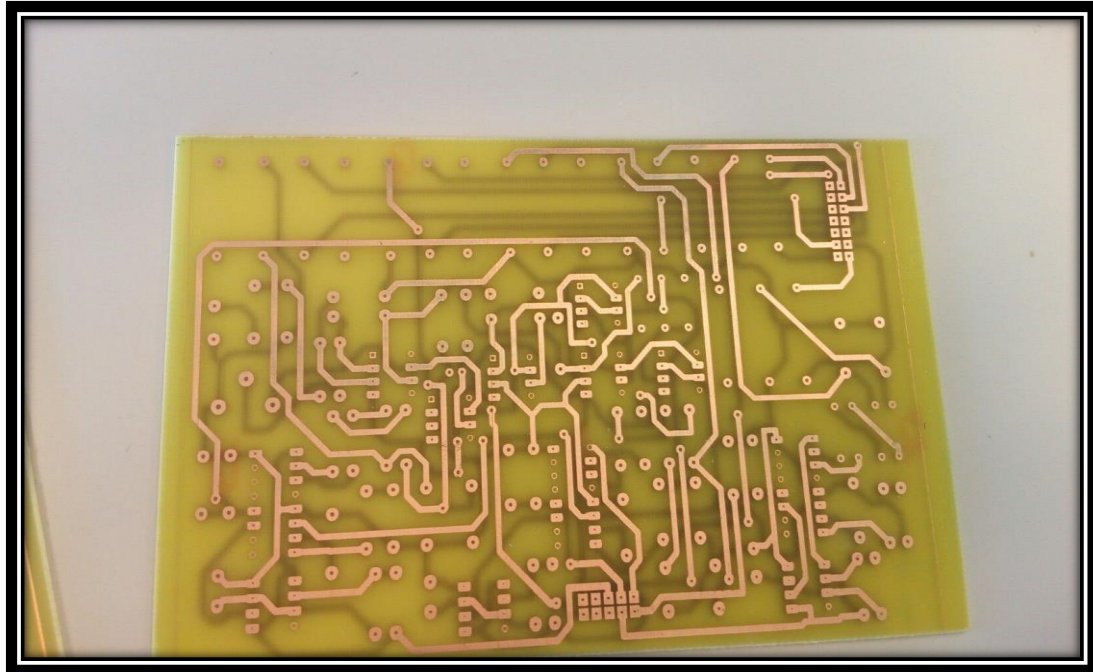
Pistas de cobre tras el atacado químico de la PCB de control
